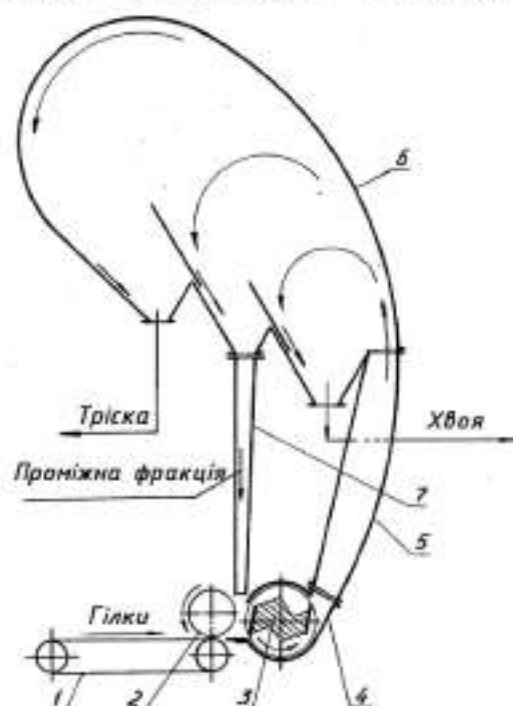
Пневмомеханічний пристрій для відділення хвої: 1 – транспортер; 2 – вал; 3 – ножовий ротор барабаний; 4 – корпус; 5 – тріскопровід; 6 – бункер; 7 – лоток
